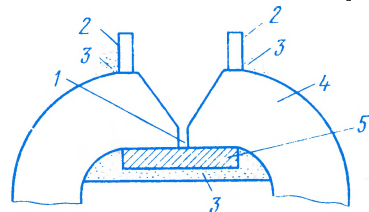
Подготовка чугунного изделия с трещиной под сварку с подогревом:
